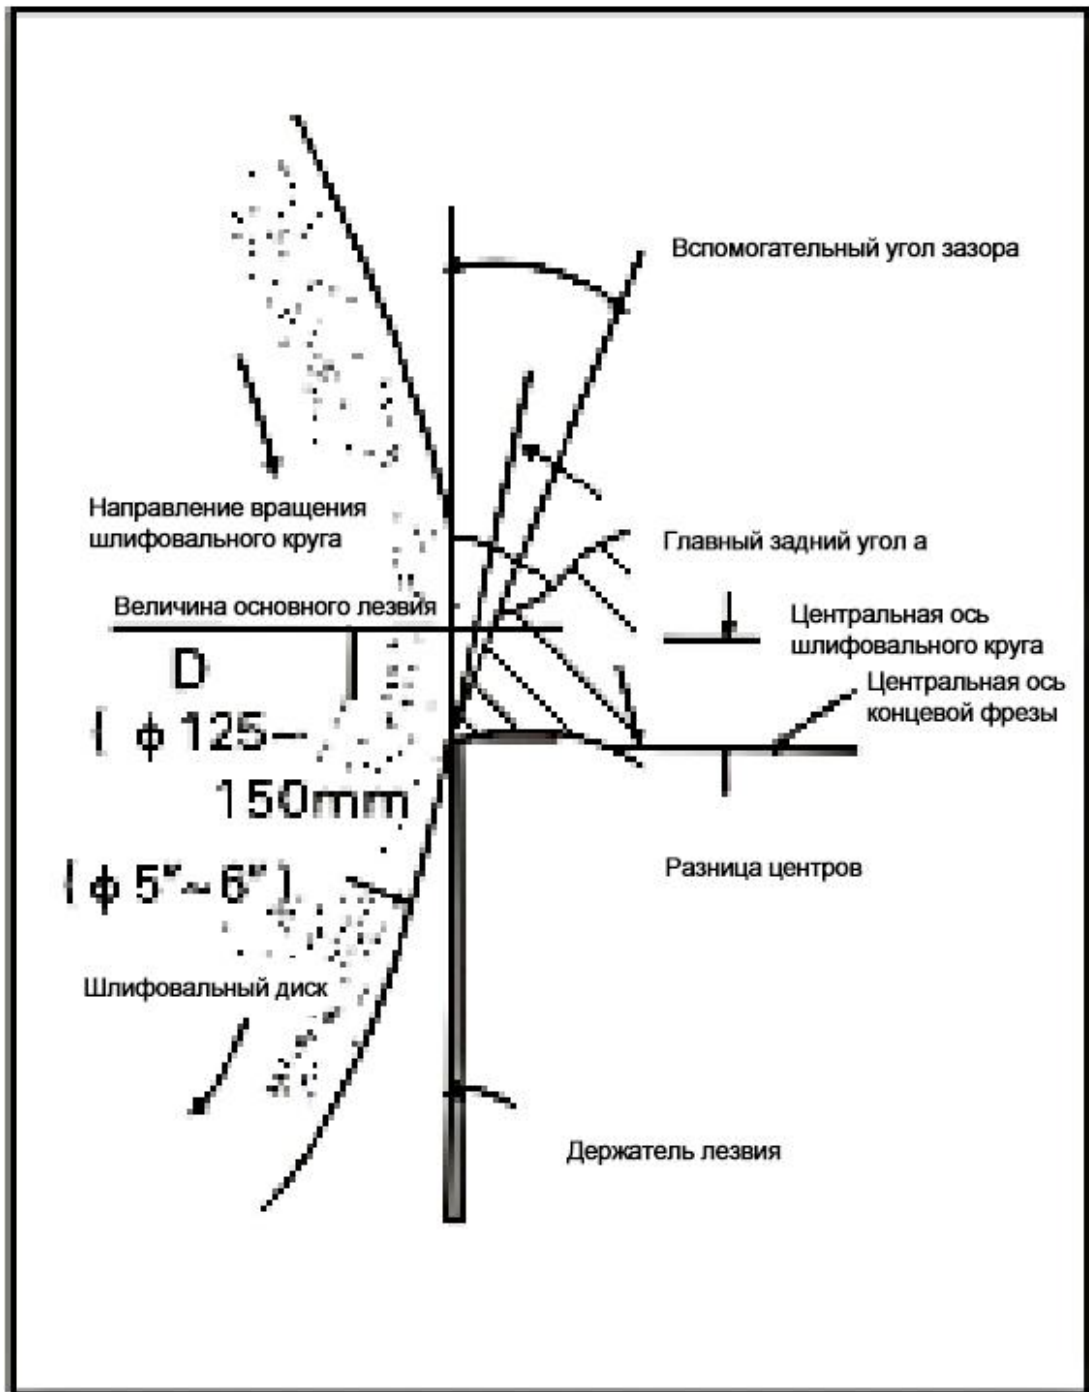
Регулировка разницы H центров 1 и 2, главный задний угол α
